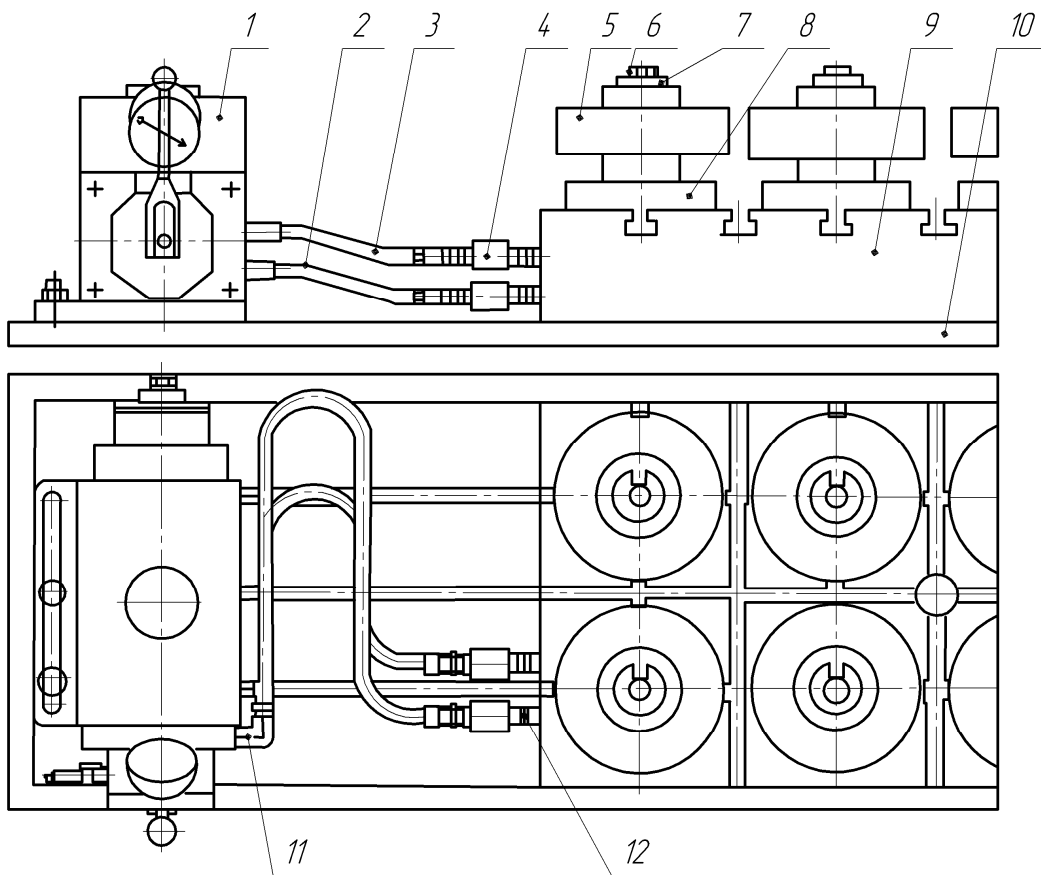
Будова гідравлічної координатної плити в робочому положенні: 1 – пневмогідро-перетворювач; 2, 3 – рукава; 4 – муфта; 5 – заготівка; 6 – болт; 7 – шайба; 8 – опора; 9 – плита гідравлічна; 10 – стіл верстата із ЧПК; 11 – штуцер; 12 – патрубок
